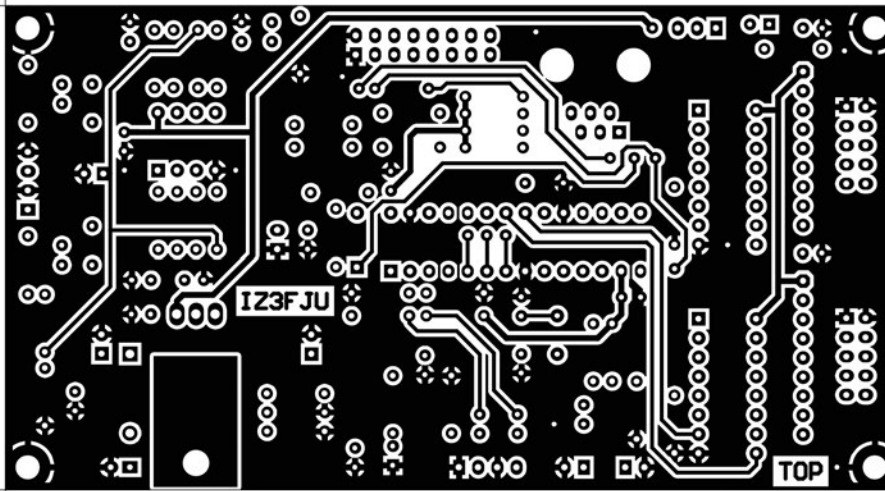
• Master in bianco/nero del lato TOP del PCB in scala 1:1
